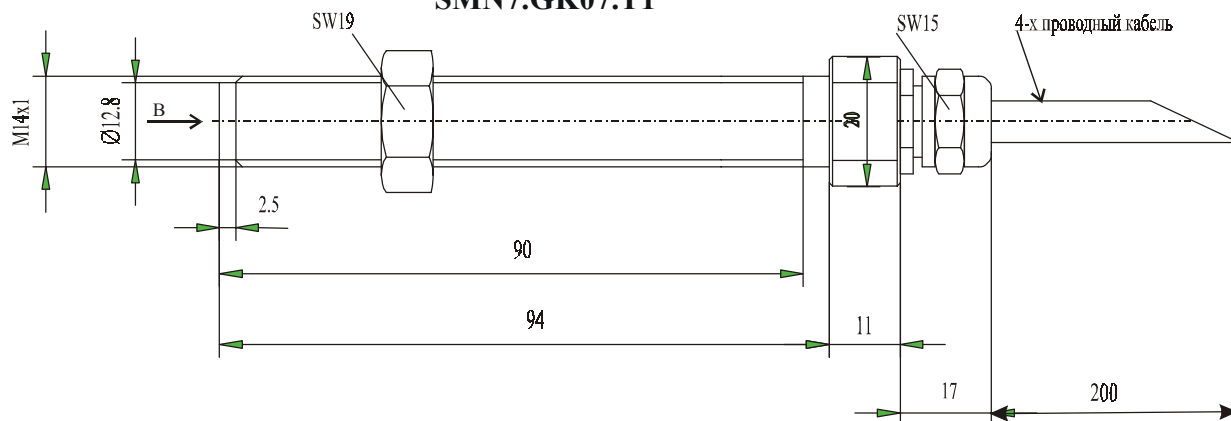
Внешний вид и габаритные размеры датчиков типа SMN7.GK07.T1
